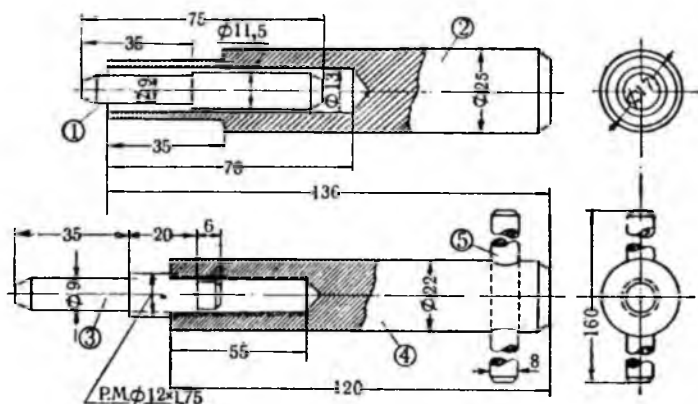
Приспособление для набивки сальников трубок радиаторов ЧТЗ:
